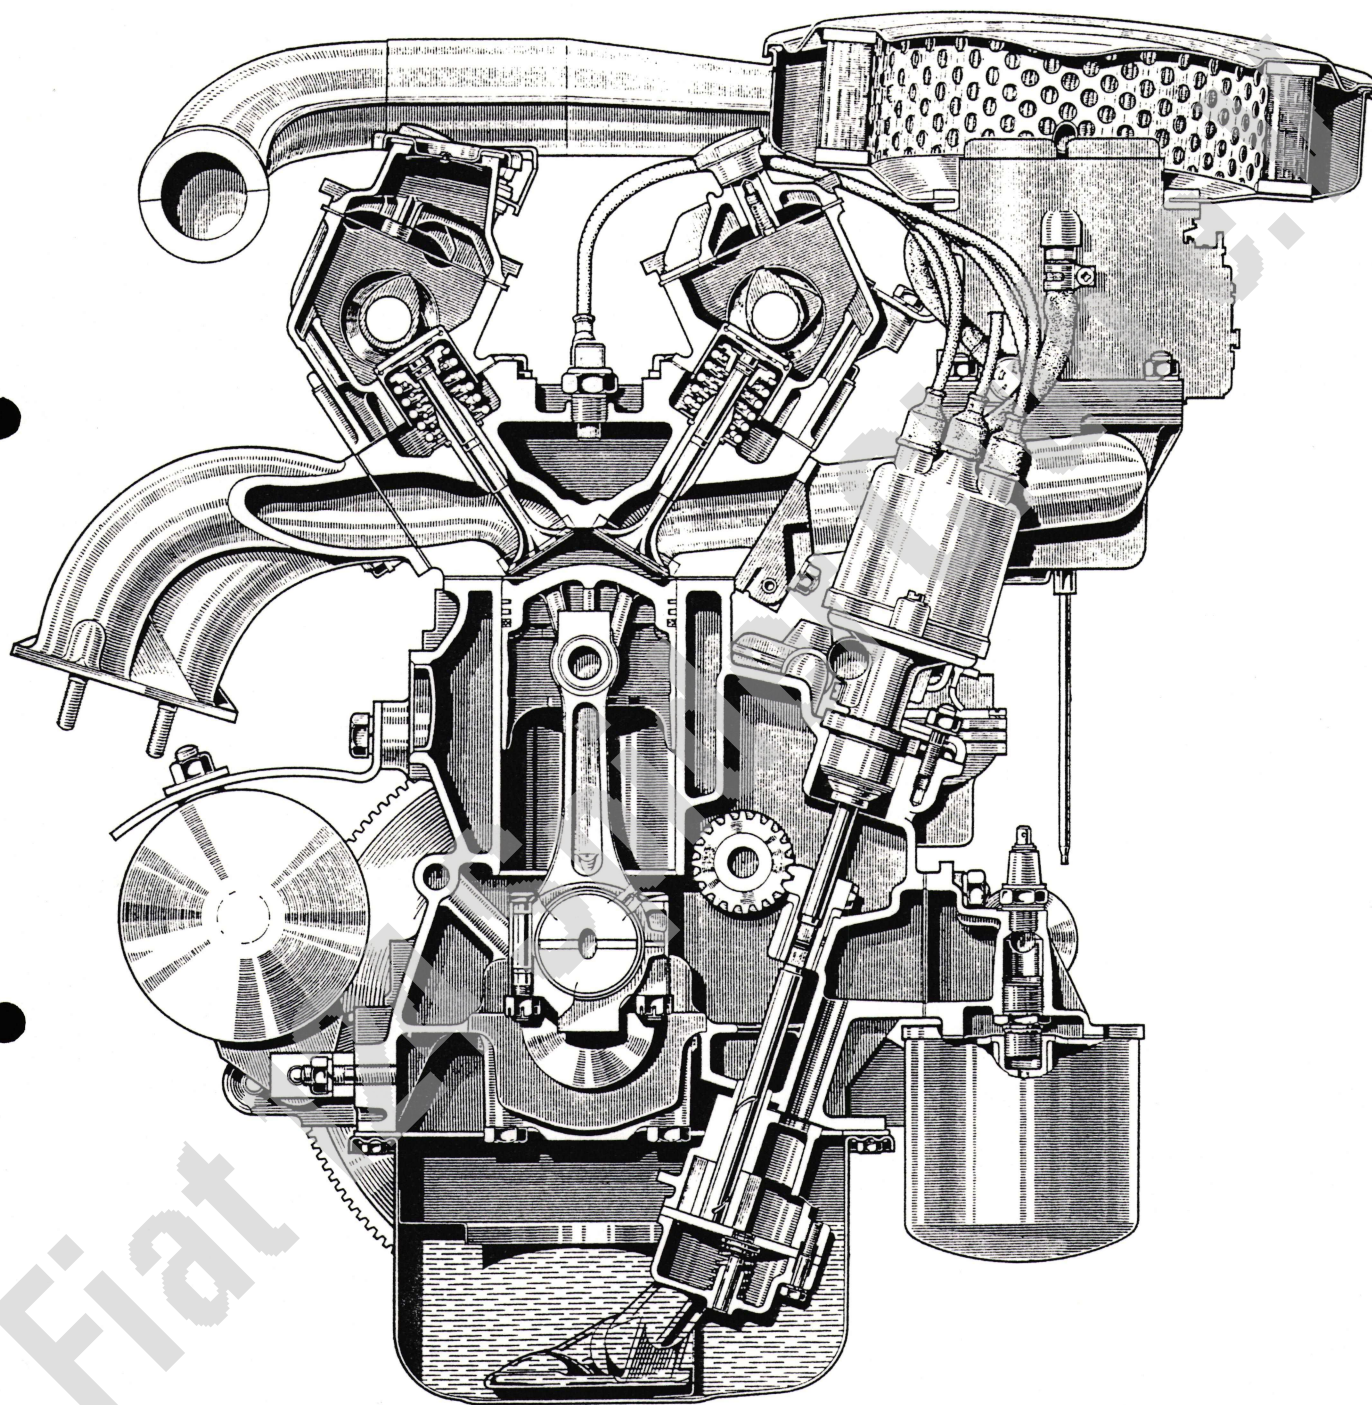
Querschnitt durch die Zylinder und die Ventile des Motors.
